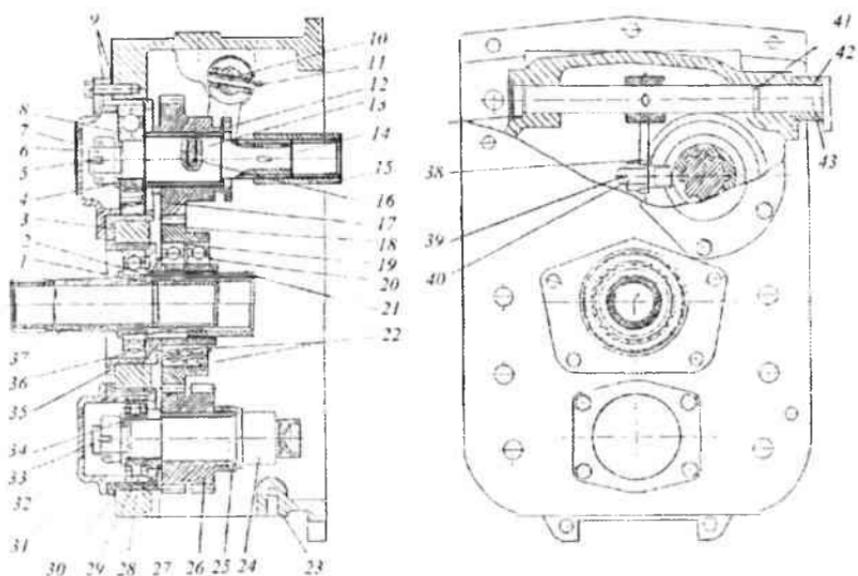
Привод раздаточного редуктора: 1, 2 – кольца; 3 – гнездо подшипника ведущего вала редуктора; 4, 34 – шайбы; 5, 10, 14, 33, 39 – шплинты; 6, 31 – гайка; 7, 32 – крышки подшипников валов редуктора; 8, 22, 28, 36 – подшипники; 9, 30 – прокладки; 11 – проволока; 12 – шарик; 13 – вал ведущий; 15 – втулка шлицевая ведущего вала редуктора; 16 – пружина фиксатора; 17 – шестерня ведущего вала редуктора; 18 – шестерня промежуточная; 19, 20 – кольца; 21 – втулка шлицевая; 23 – проставка; 24 – вал; 25, 27 – втулки упорные; 26 – шестерня; 29 – гнездо переднего подшипника нижнего вала; 35 – гнездо подшипника трубчатого вала; 37 – вал трубчатый; 38 – рычаг; 40 – палец включения блокировки дифференциала; 41 – кольцо уплотнительное; 42 – втулка; 43 – вал с рычагом
